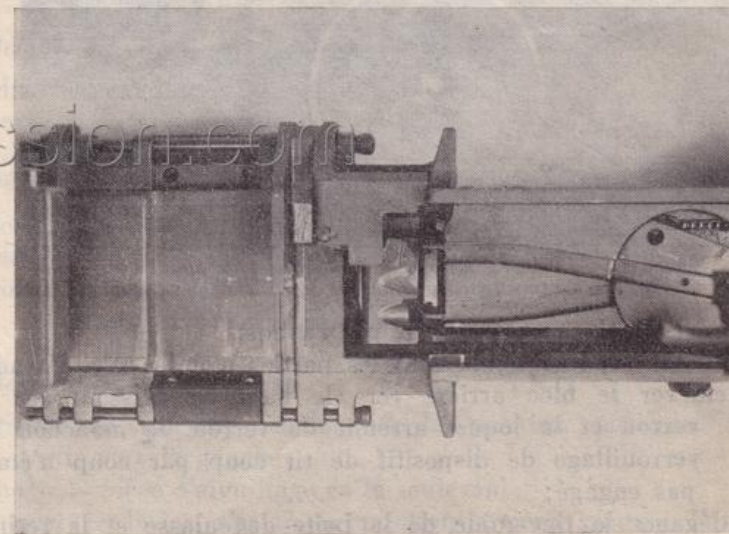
Pour visser ou dévisser le canon, tirer l'ensemble mobile vers l'arrière, d'environ 8 mm.
